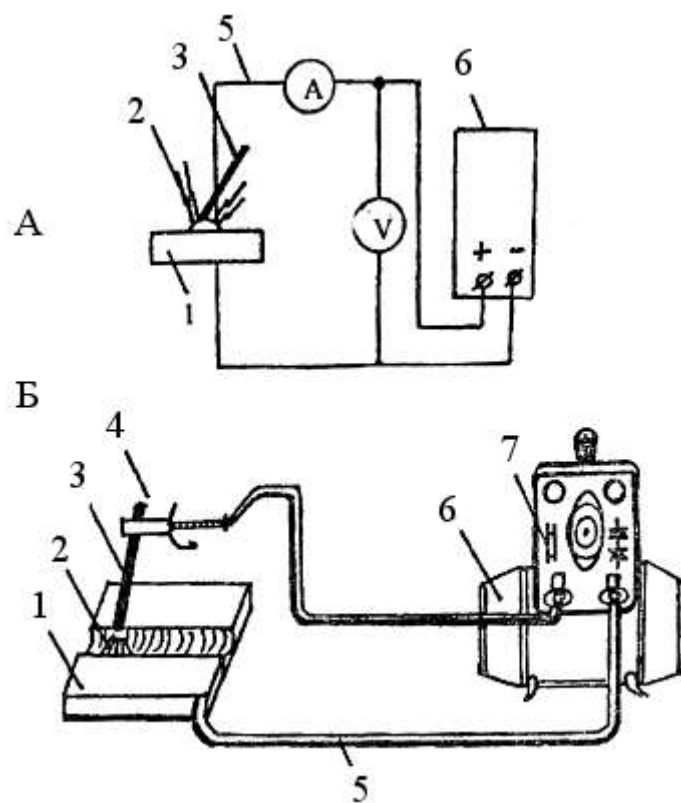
Электрическая цепь для зажигания сварочной дуги.
